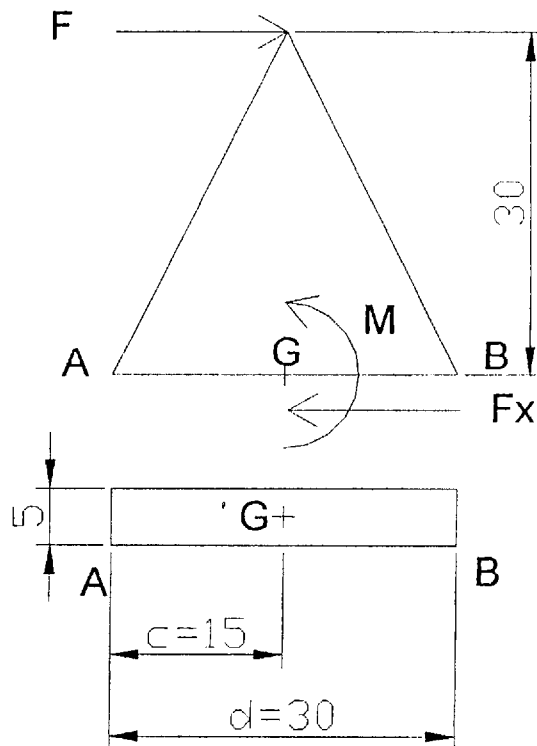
Dimensiones para el Cálculo de la Soldadura
